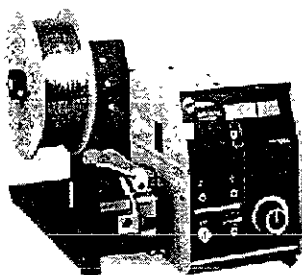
alimentador del microalambre para una máquina de proceso GMAW
